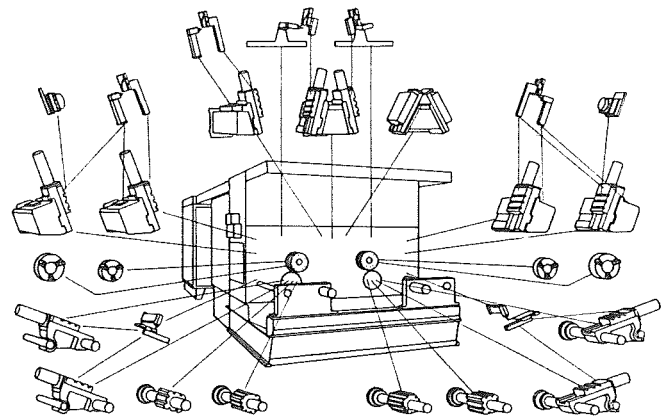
Frontdrehmaschine mit Einrichtungen nach dem Baukastenprinzip
